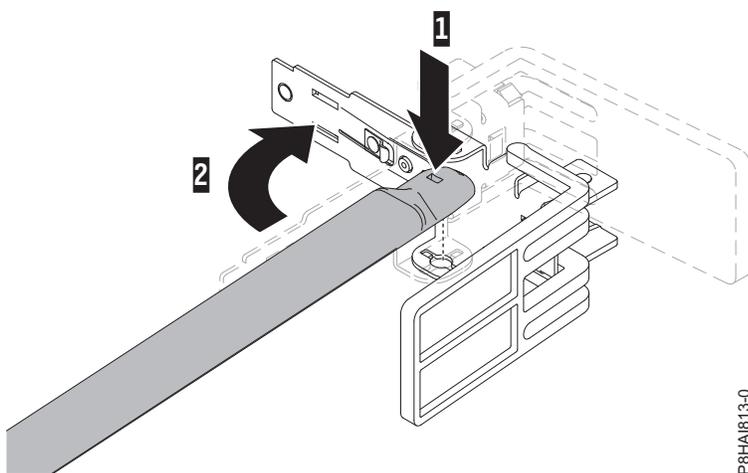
Suporte de paragem de gestão de cabos presa ao braço de suporte
